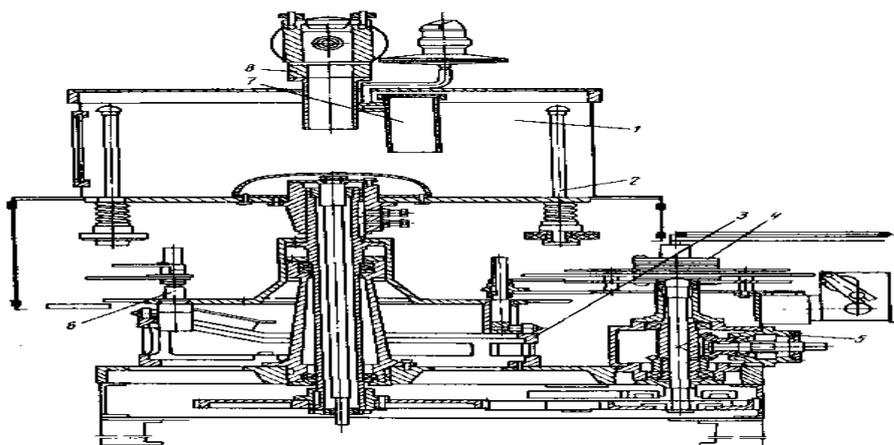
Наповнювальний апарат ДН 1:бак; 2) дозатор; 3) копір; 4) механізм прийому; 5) привід; 6)столики.
